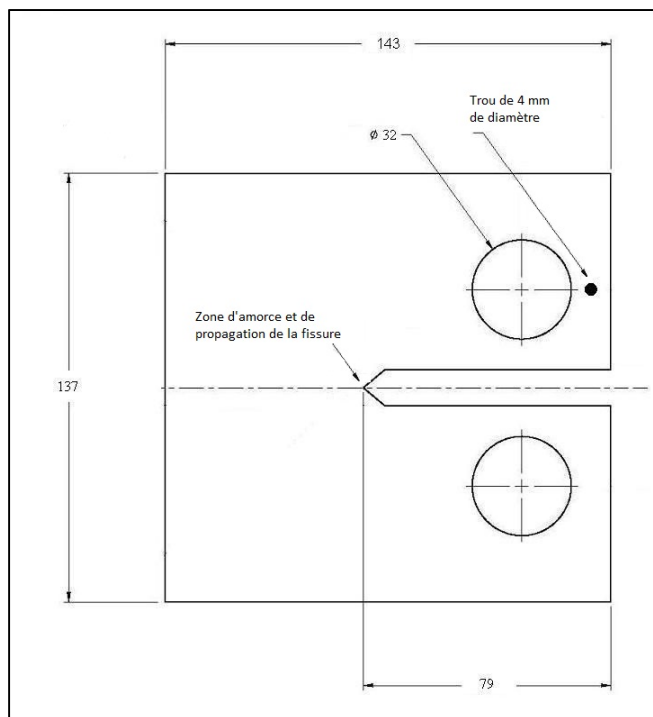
Dessin schématique du spécimen compact de tension (dimensions en mm)
